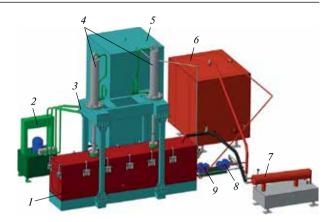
3D-модель сушильно-прессовой установки СПК-1М:
